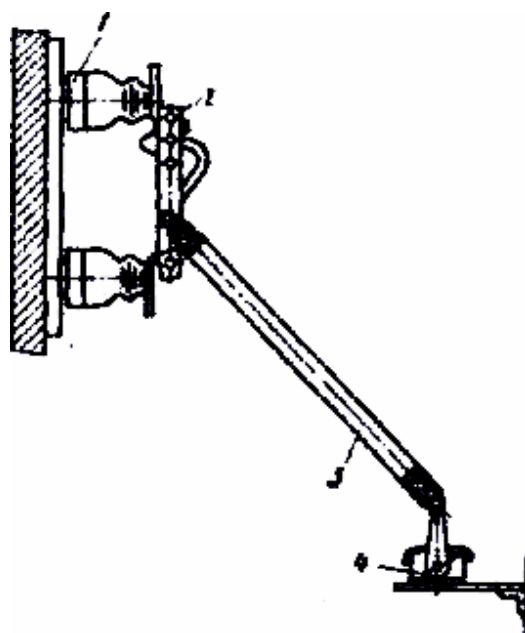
Установка вспомогательных контактов к однополюсному разъединителю
